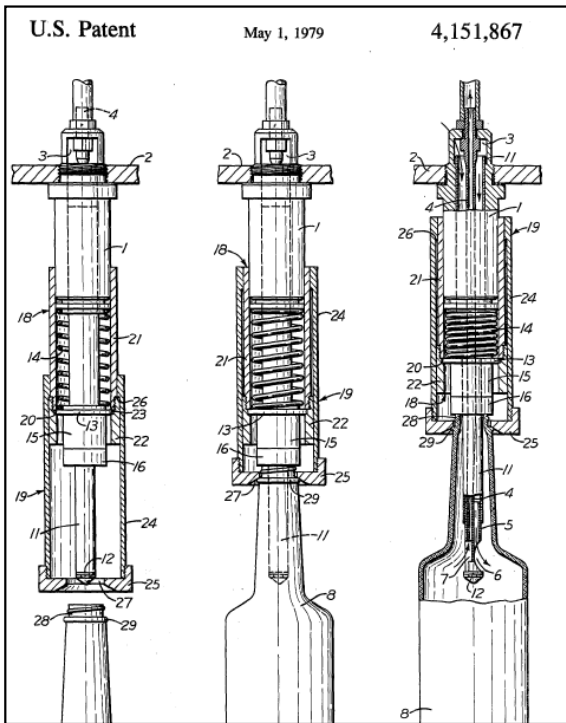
Bottle Filler Valve [ref \[28\]](#)
